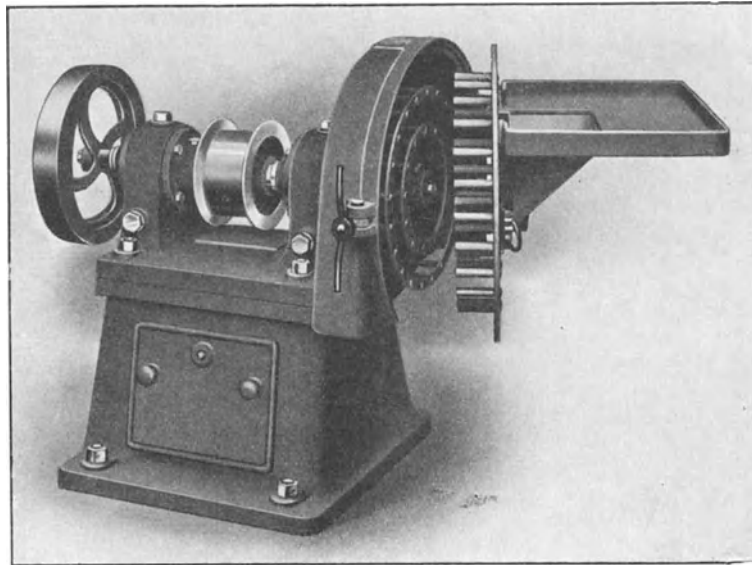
Sandschleudermaschine mit ausschwenkbarem Stiftenkorb.
